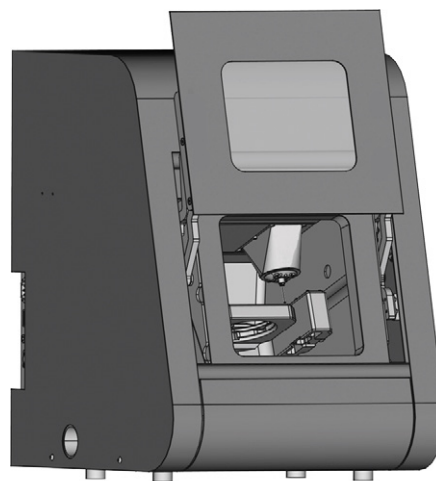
ДВЕРЬ РАБОЧЕЙ КАМЕРЫ
